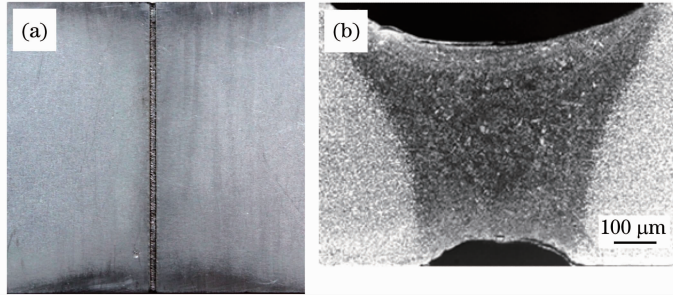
激光焊接 DP600 接头形貌。(a)表面;(b)截面
